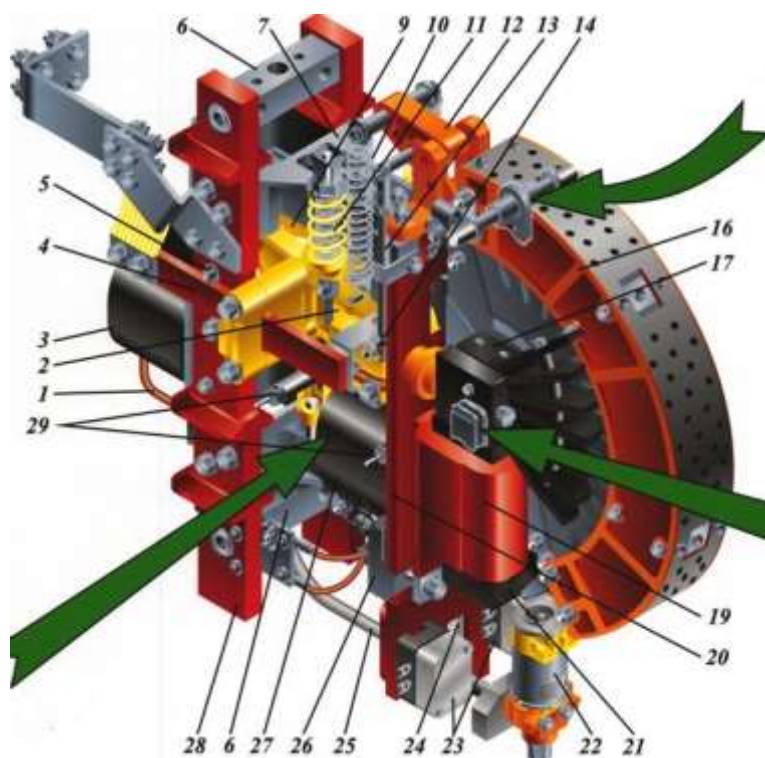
Общий вид быстродействующего выключателя ВБ-8
